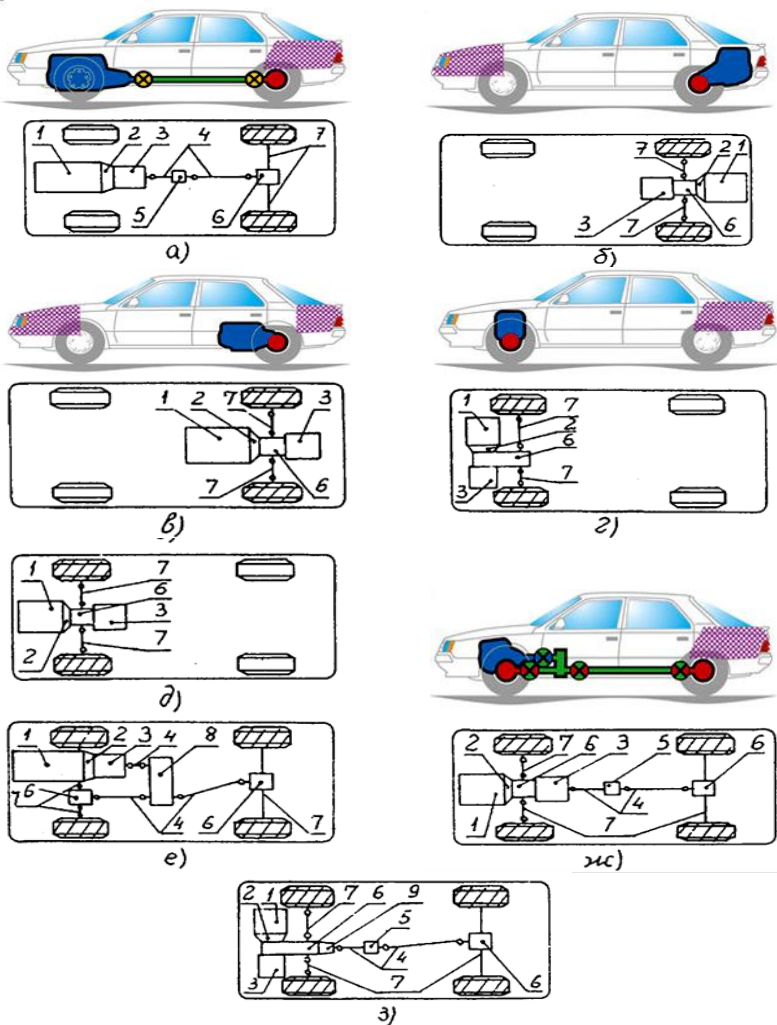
Компоновка легковых автомобилей: а - классическая; б - заднемоторная; в - центральномоторная; г, д - переднеприводные; е, ж, з - полноприводные; 1 - двигатель; 2 - сцепление; 3 - КП; 4 - карданная передача; 5 - промежуточная опора карданной передачи; 6 - центральная (главная) передача; 7 - привод ведущих колес; 8 - раздаточная коробка; 9 - коробка отбора мощности
